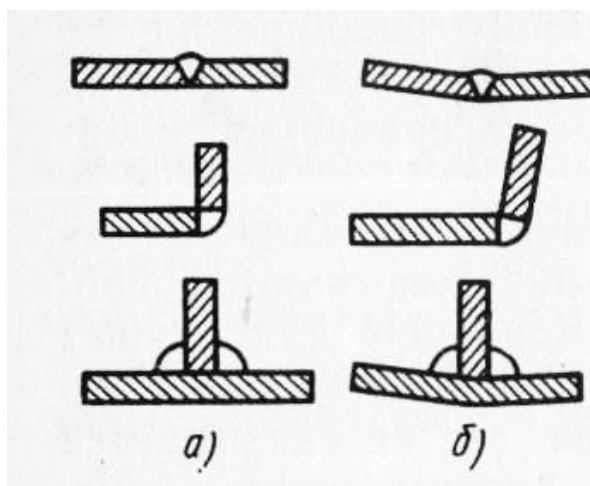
Деформация металлоконструкции: а) – Металлоконструкция перед сваркой. б) – Сварная металлическая конструкция
